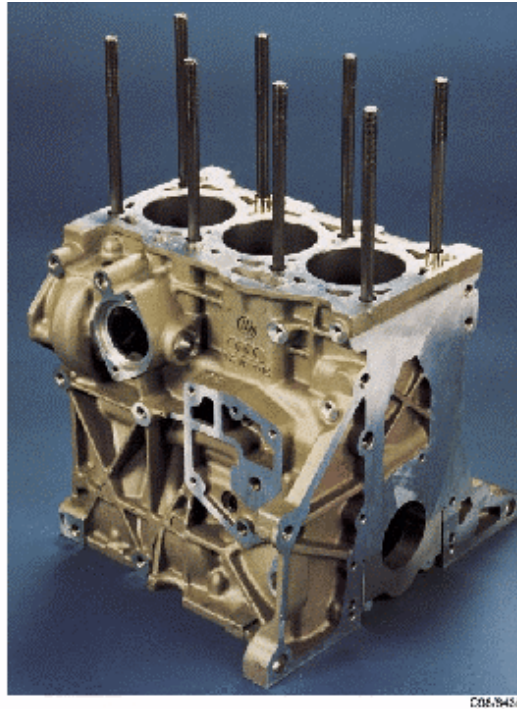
Aluminium – Zylinderkurbelgehäuse
